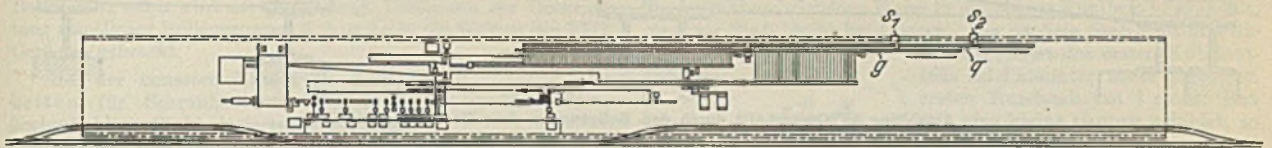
Halbkontinuierliche Stabstraße mit zwei in einem Strang angeordneten Zwischengerüsten, zwei Einstichtriogerüsten und einer dreigerüstigen Zickzack-Duostraße.
